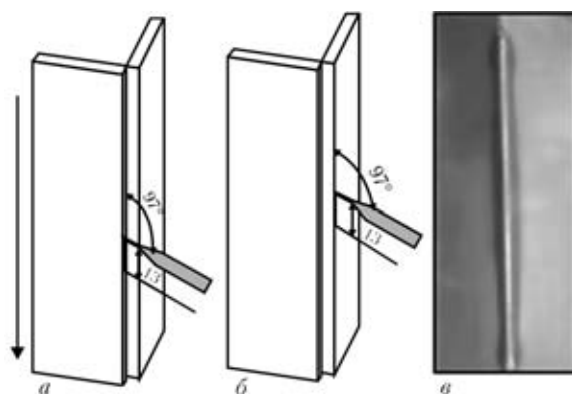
Выполнение модифицированной МАГ сваркой углового соединения при нулевом зазоре в корне (а, б) и внешний вид соединения (в)
